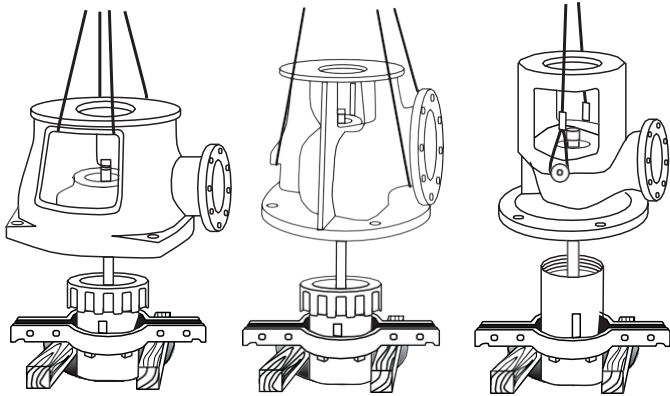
Montaje de la cabeza de tubería a la tubería de columna
